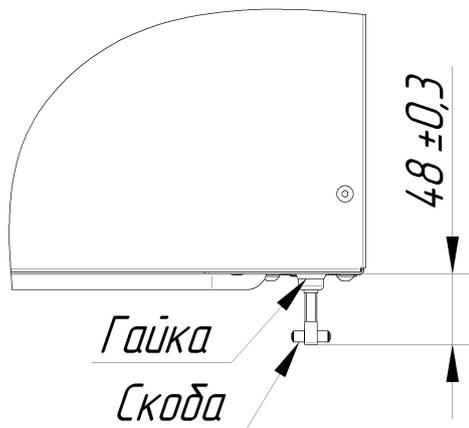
Регулировка замкового устройства (для КЭП-4ПМ-01)
